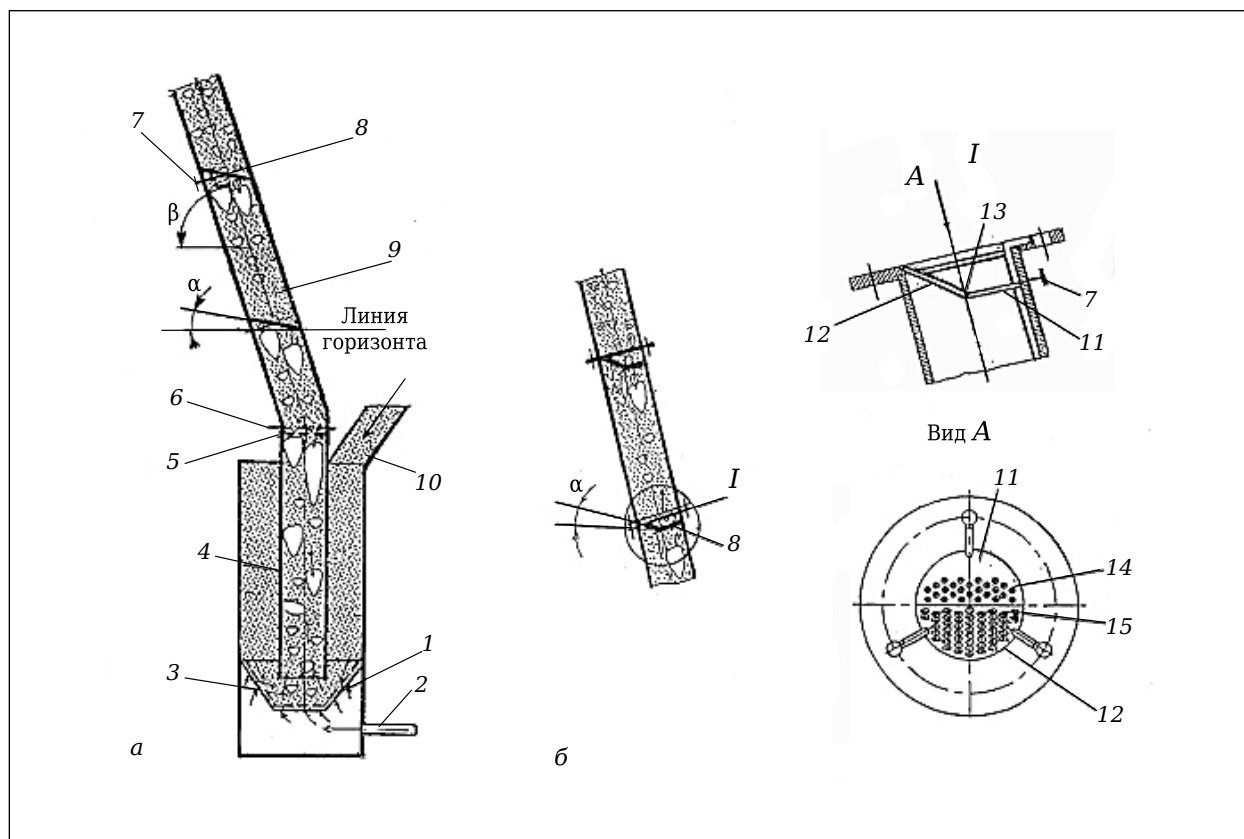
Наклонный пневмоподъемник: *а* — общий вид установки; *б* — вариант выполнения вставок; 1 — пористая газораспределительная перегородка; 2 — патрубок для подвода сжатого воздуха; 3 — смесительная камера; 10 — загрузочный патрубок; остальные обозначения — в тексте
